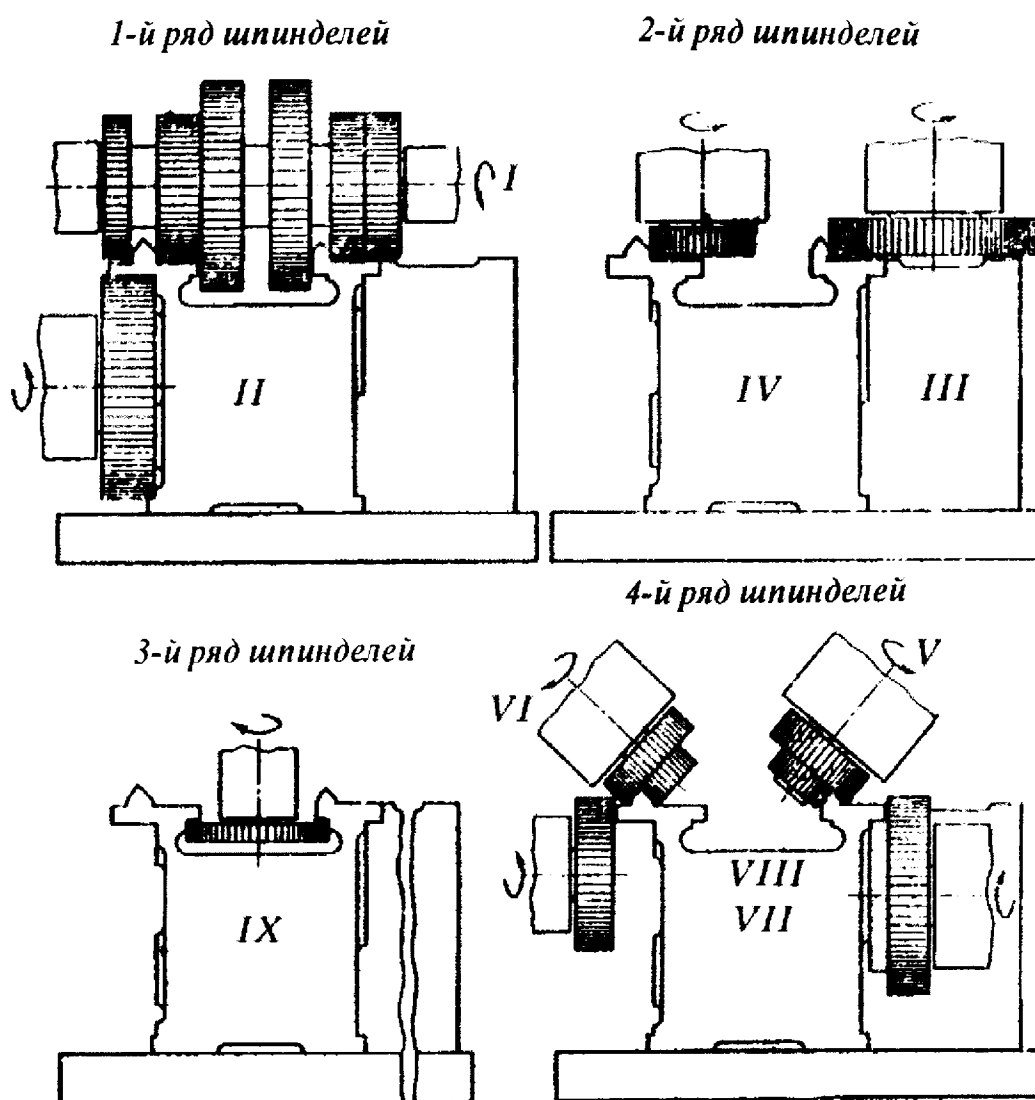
Схема черновой обработки станины на девятишпиндельном продольно-фрезерном станке
